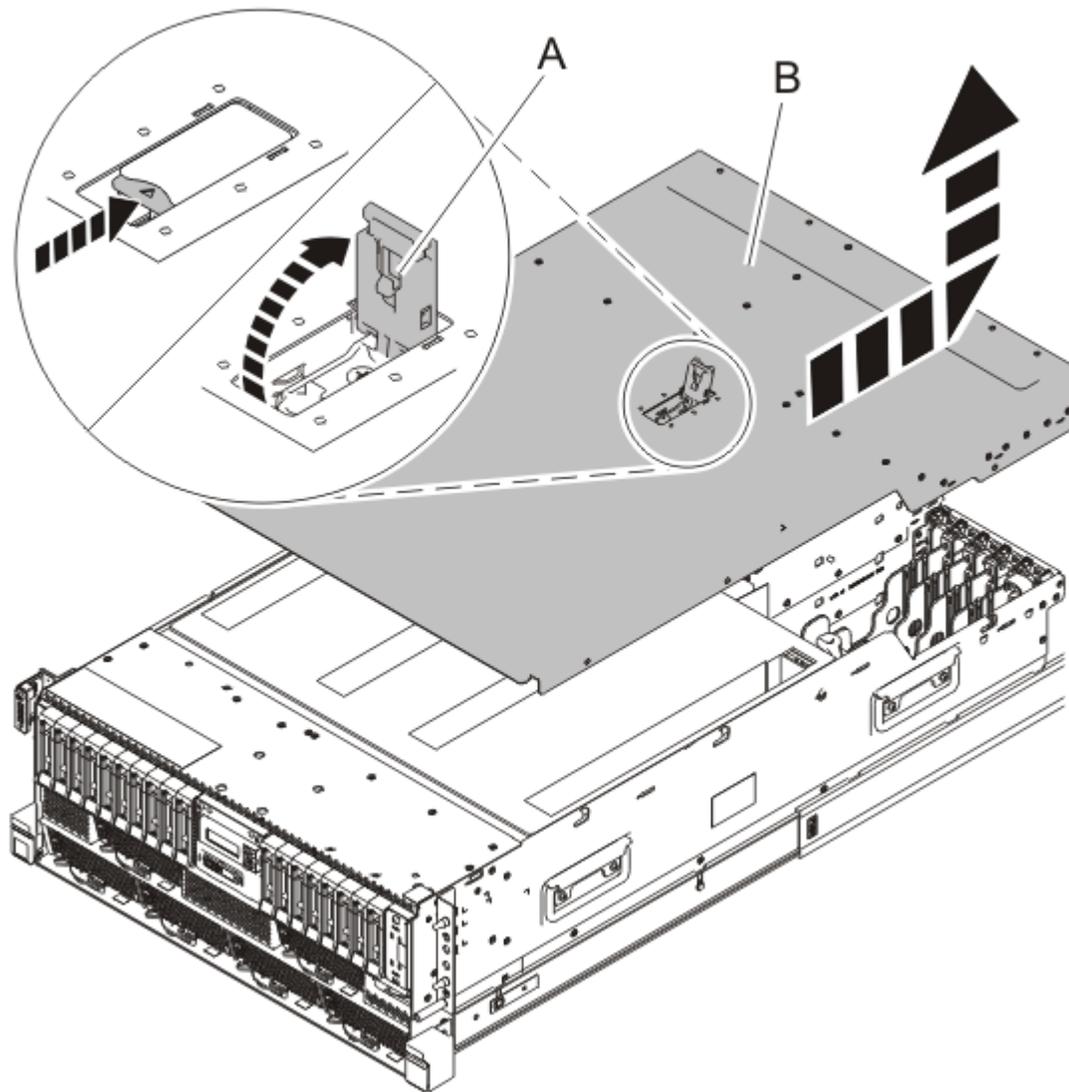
Removendo a Tampa de Acesso de Serviço de um Sistema Montado em Rack
